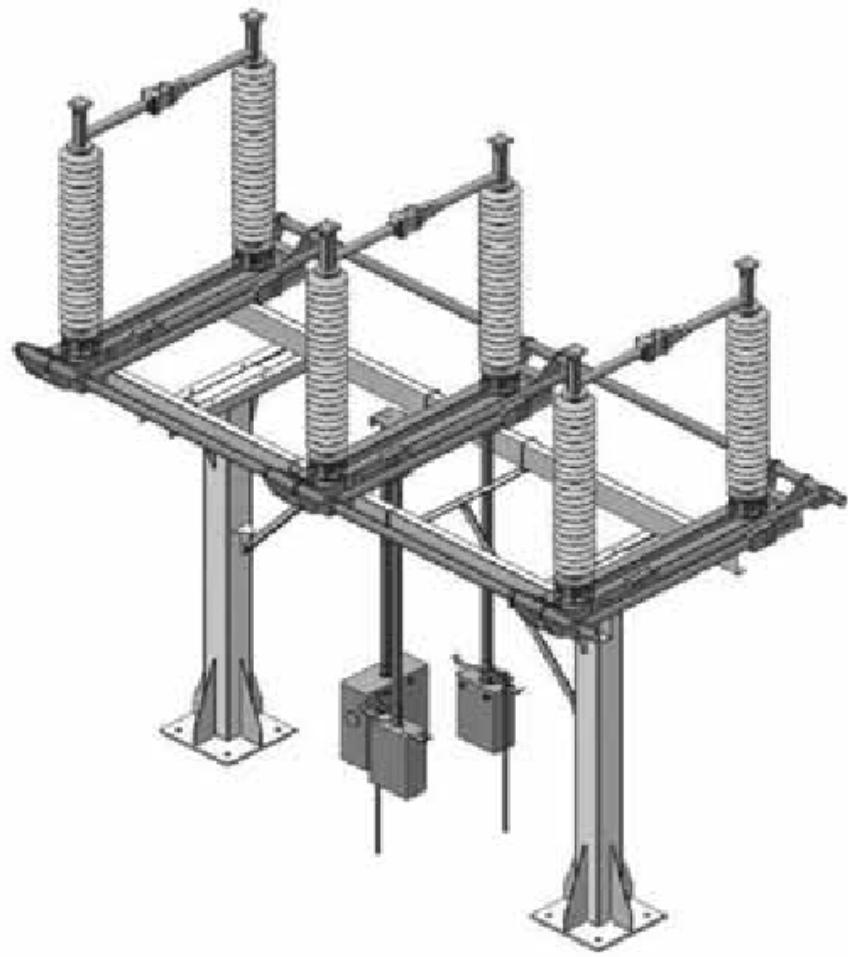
Разъединитель марки РПД-110/1000 УХЛ 1
